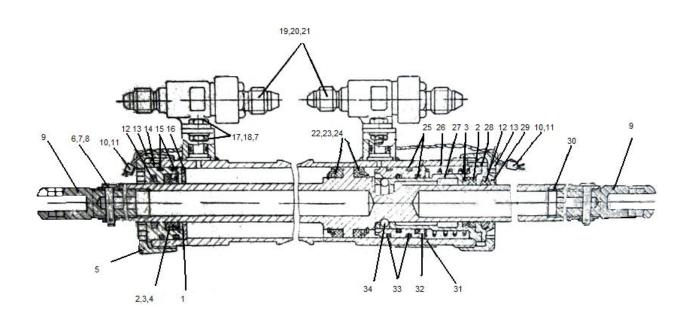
Цилиндр выпуска и уборки посадочных щитков
